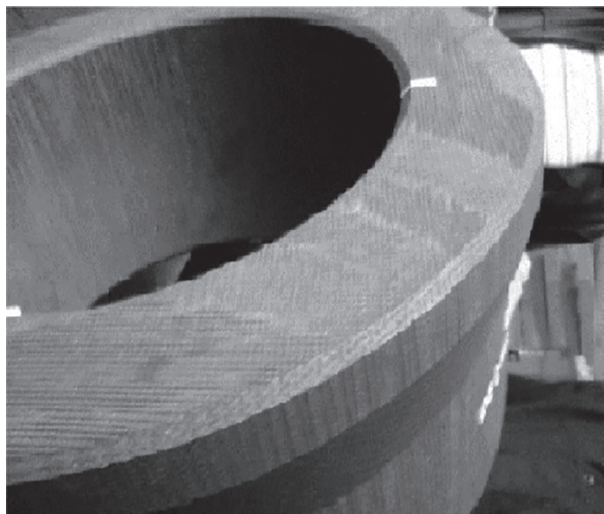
Крупногабаритная заготовка из трехмерно армированного УУКМ.
